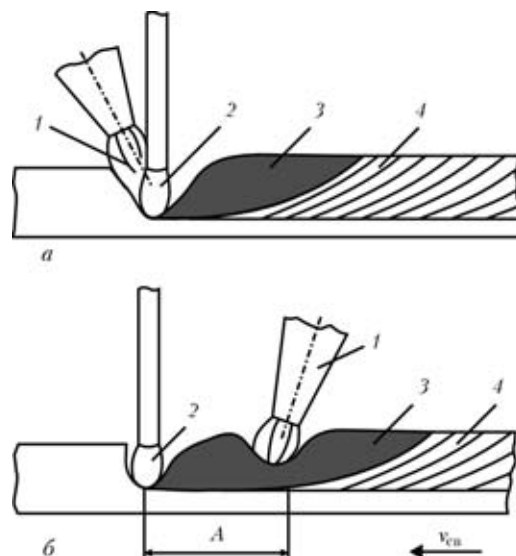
Схема гибридной сварки дуга + газовое пламя: а — газовое пламя расположено перед дугой; б — за дугой; 1 — газовое пламя; 2 — электрическая дуга; 3 — сварочная ванна; 4 — шов
